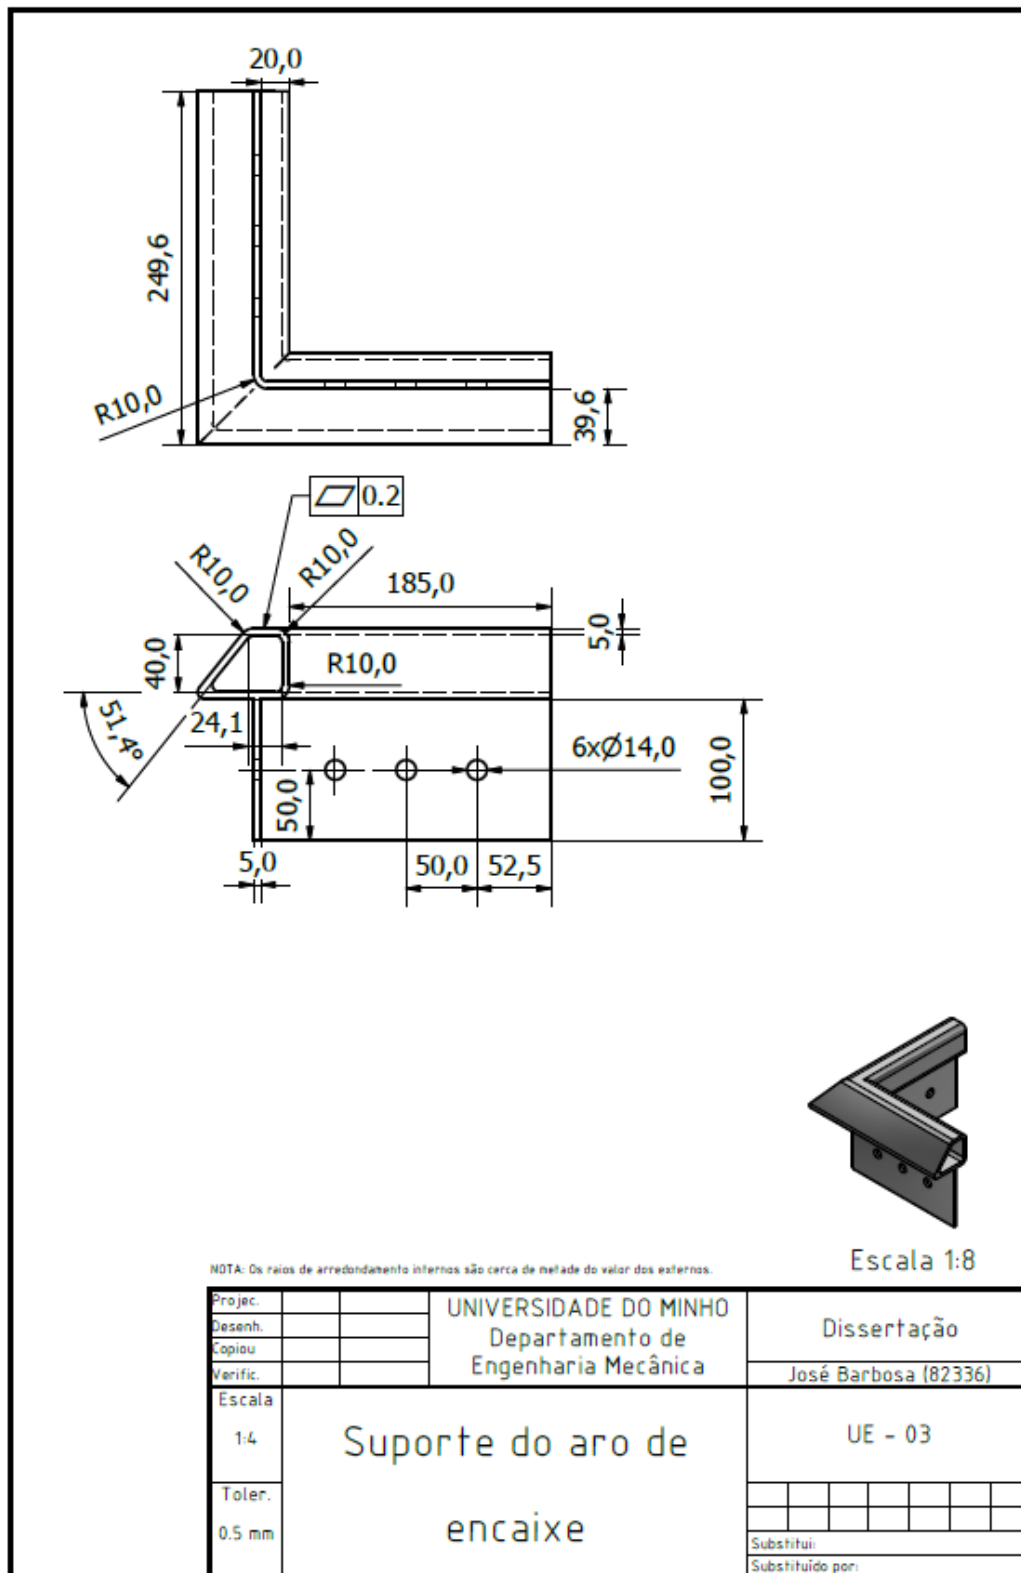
Figura Anexo III-3 – Desenho técnico do suporte do aro de encaixe.
